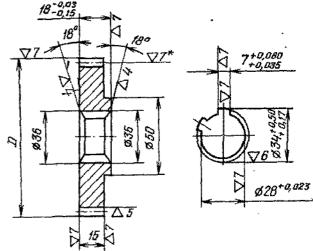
Типовой чертеж сменной шестерни * Для станка 16К20П ▽ 8
